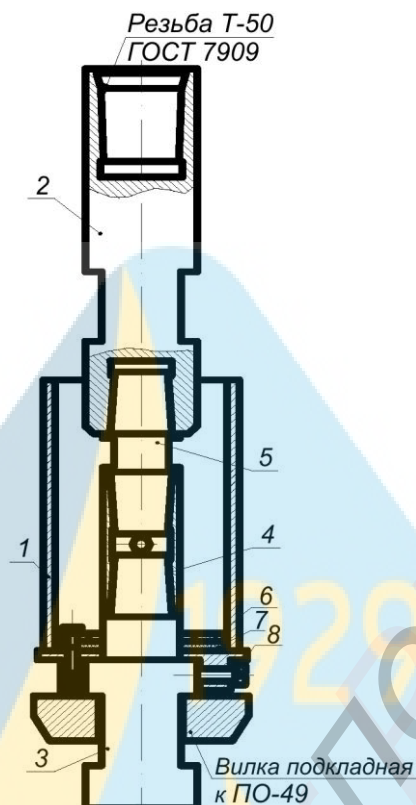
Приставка до стенду для визначення середнього напрацювання замкового різьблення на відмову: 1 – склянка; 2 - подовжувач; 3 - опора нижня; 4 – муфта; 5 - ніпель; 6 - диск; 7 - прокладення; 8 – болти; 9 - гайки
